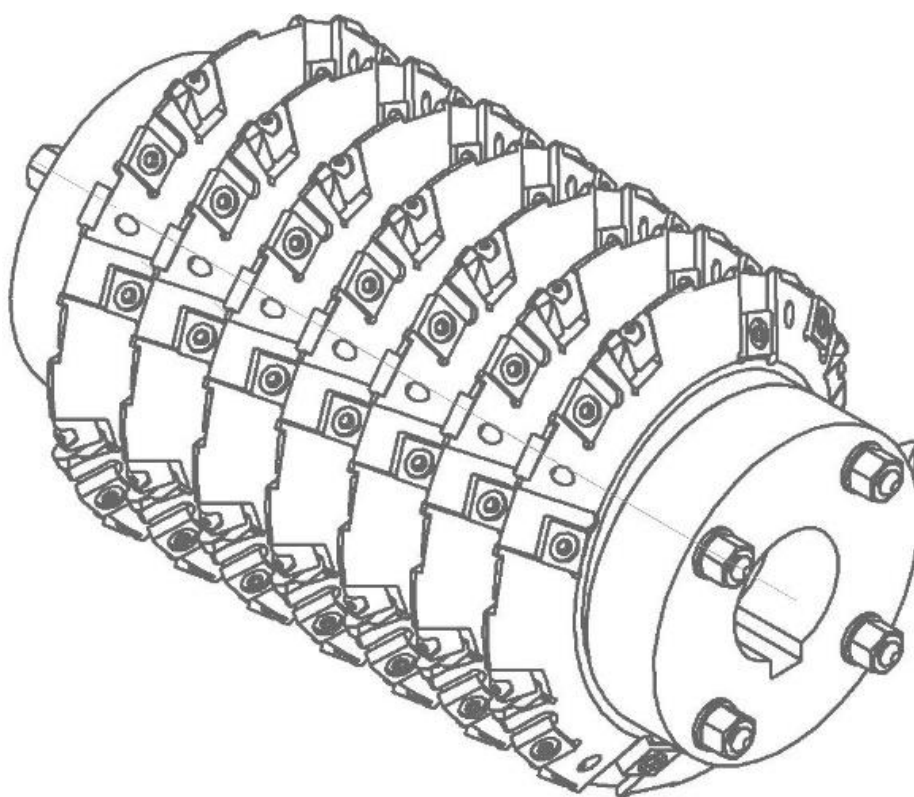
Инструмент для формообразования зубчатых колес с нестандартными исходными контурами зацепления
